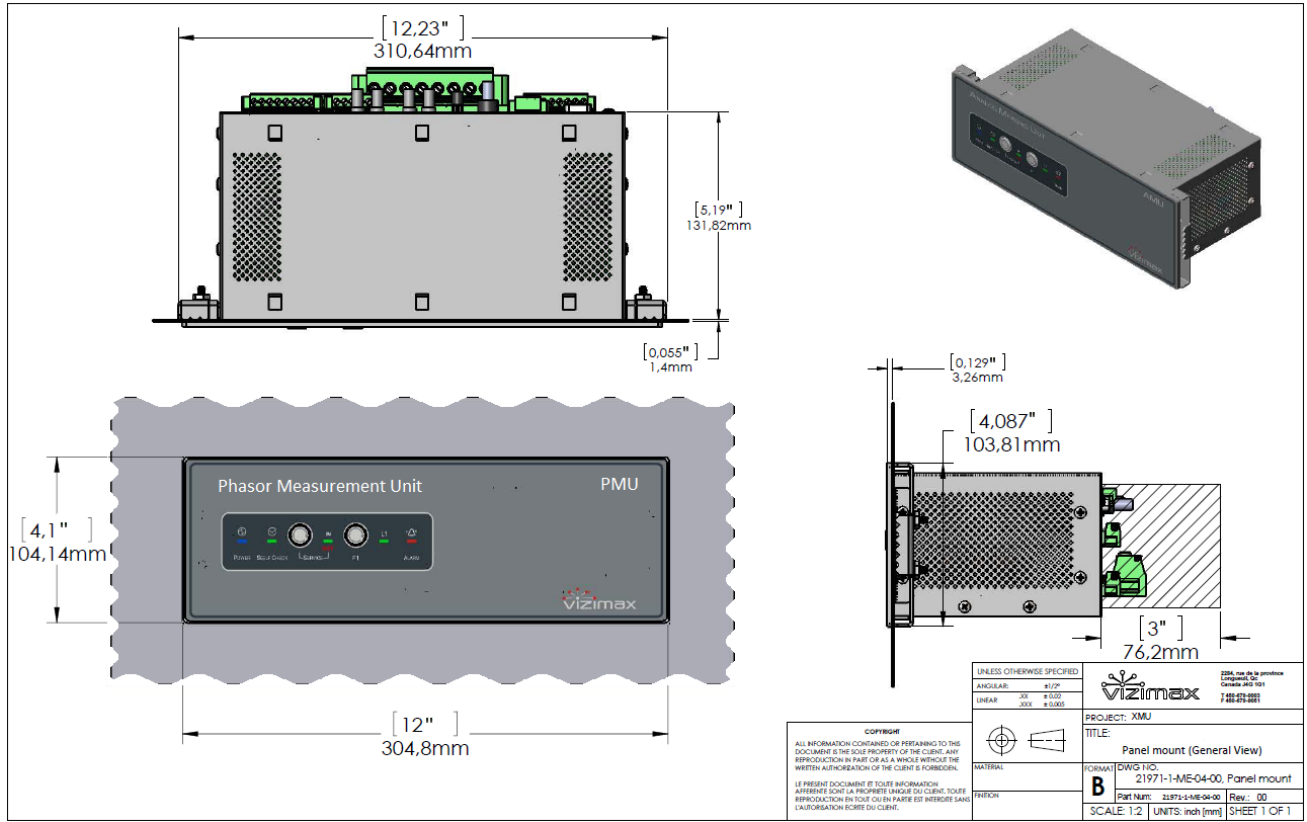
CONFIGURATION POUR MONTAGE SUR PANNEAU
